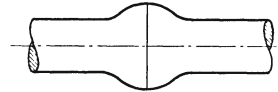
Stumpfschweißung von Eisen und Stahl.
